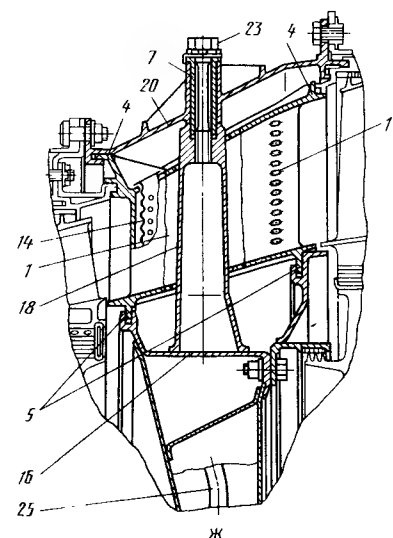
Крепление сопловых лопаток в корпусах:
